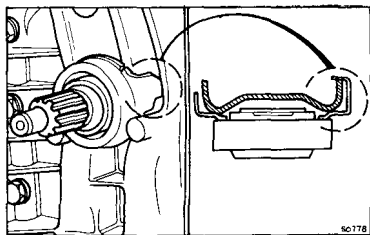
Установочный зажим выжимного подшипника сцепления
